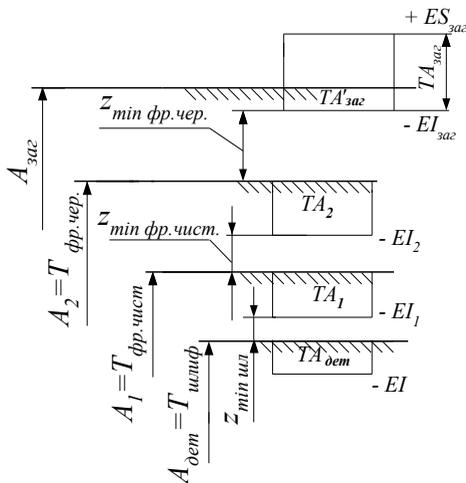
Расчетная схема для определения размера заготовки с использованием минимальных припусков (охватываемый размер детали)
